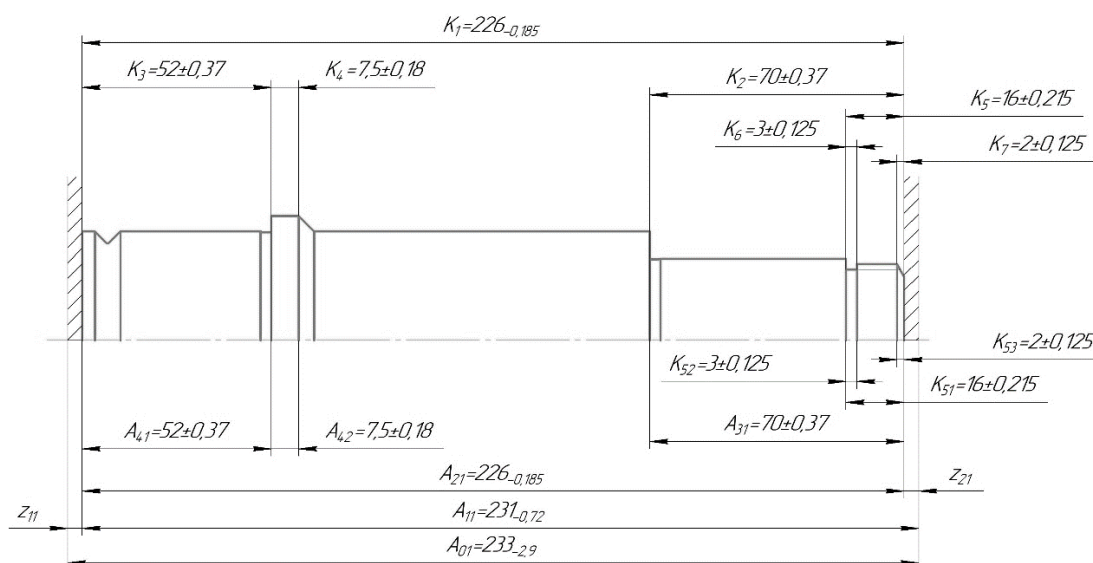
Размерная схема технологической детали «Шпиндель заготовительного станка»
